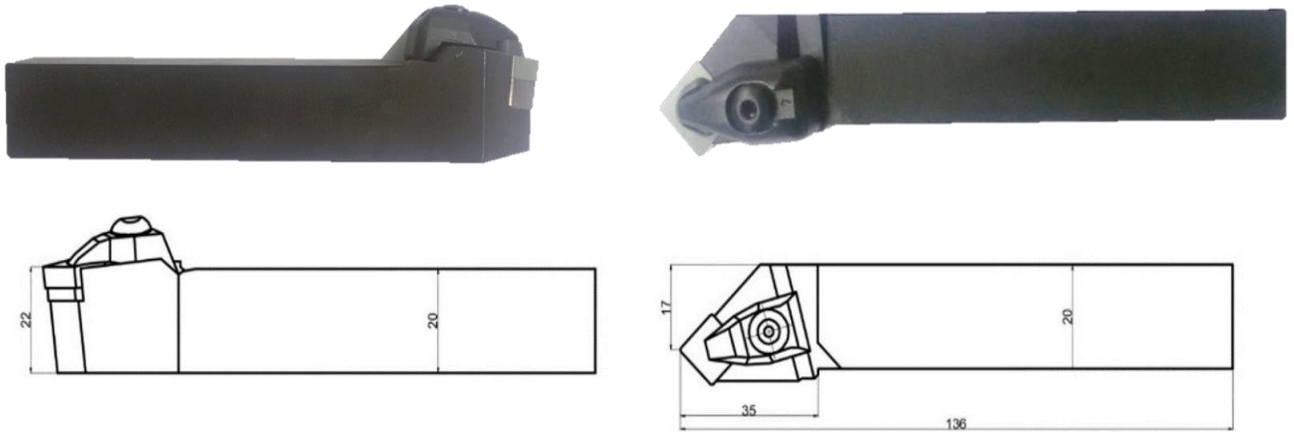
Внешний вид и габаритные размеры державки формой CSBNR2525M12.
